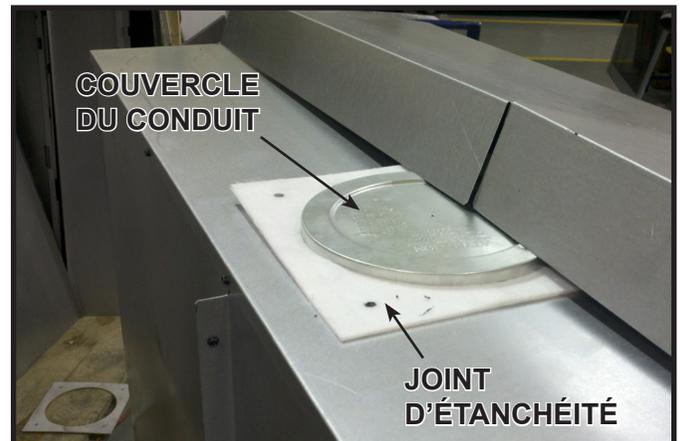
Emplacement du couvercle du conduit et du joint d'étanchéité
